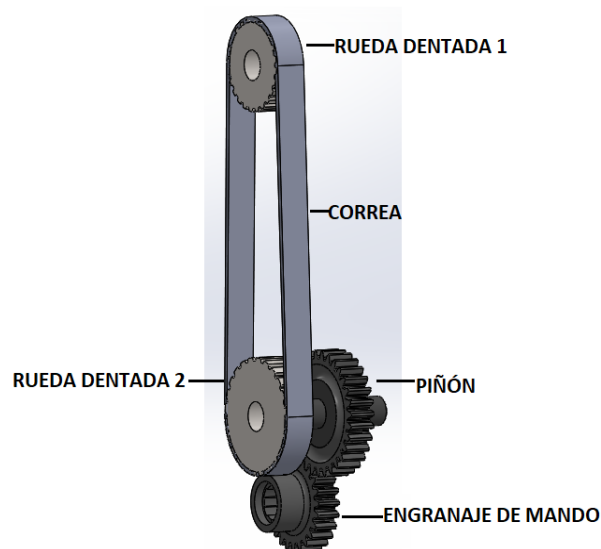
Disposición de engranajes. Diseñado por la autora para este TFG
